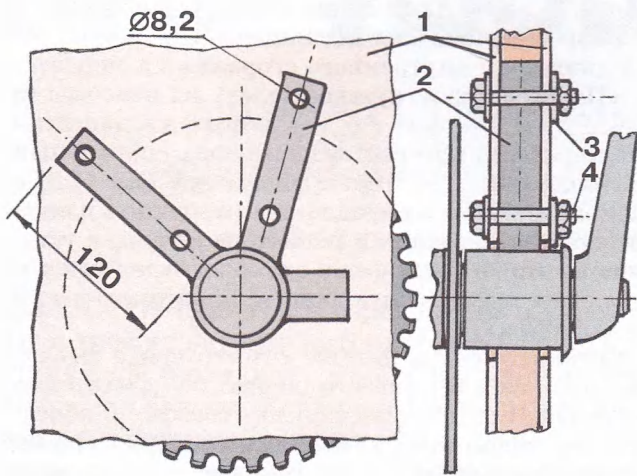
Способ крепления втулки педалей: 1 — боковины центральной части поплавка; 2 — фрагмент велорамы со втулкой педалей; 3 — шайба; 4 — крепежный болт М-8.
